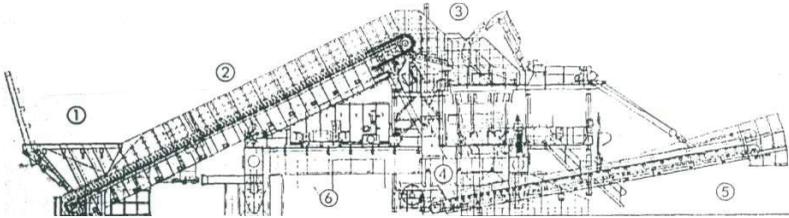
Схема самоходного дробильного агрегата: 1 – загрузочный бункер; 2 – конвейер; 3 – дробилка; 4,5 – разгрузочный и поворотный конвейеры; 6 – несущая конструкция
